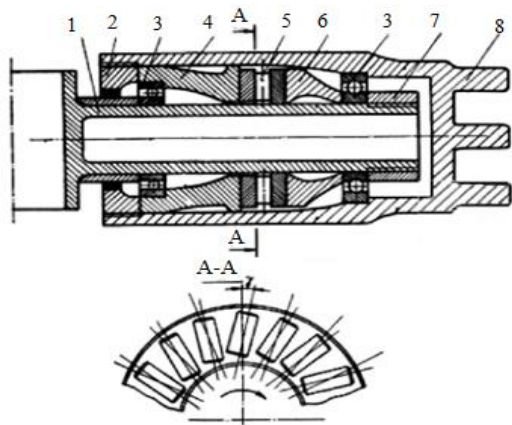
Конструкція осьового шарніра втулки НГ вертольоту Мі-24А: 1 – цапфа, 2 – гайка корпусу осьового шарніра, 3 – радіальний шарикопідшипник, 4 – розпірна втулка, 5 – упорний роликовий підшипник, 6 – упорне кільце, 7 – гайка, 8 – корпус
